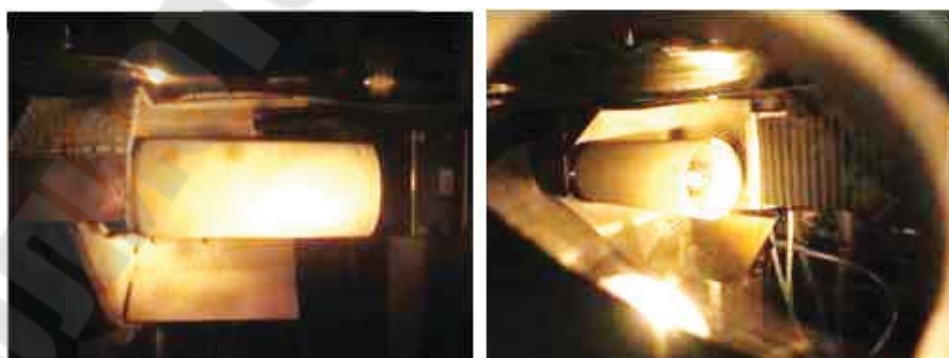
Цилиндрическая заготовка, полученная методом *Spray forming
